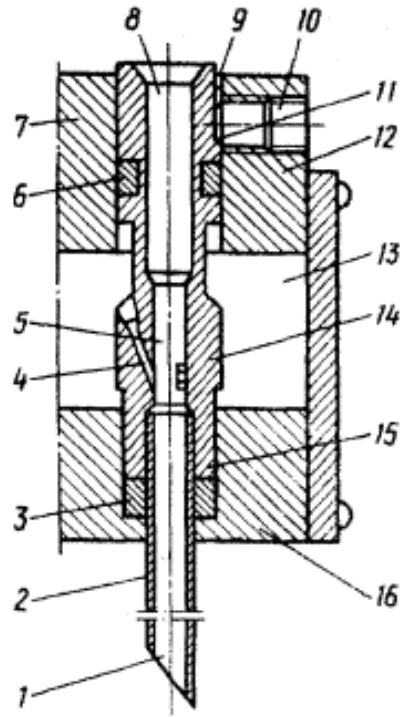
Схема иглы и игольного бруса тафтинговой машины пневматического действия
